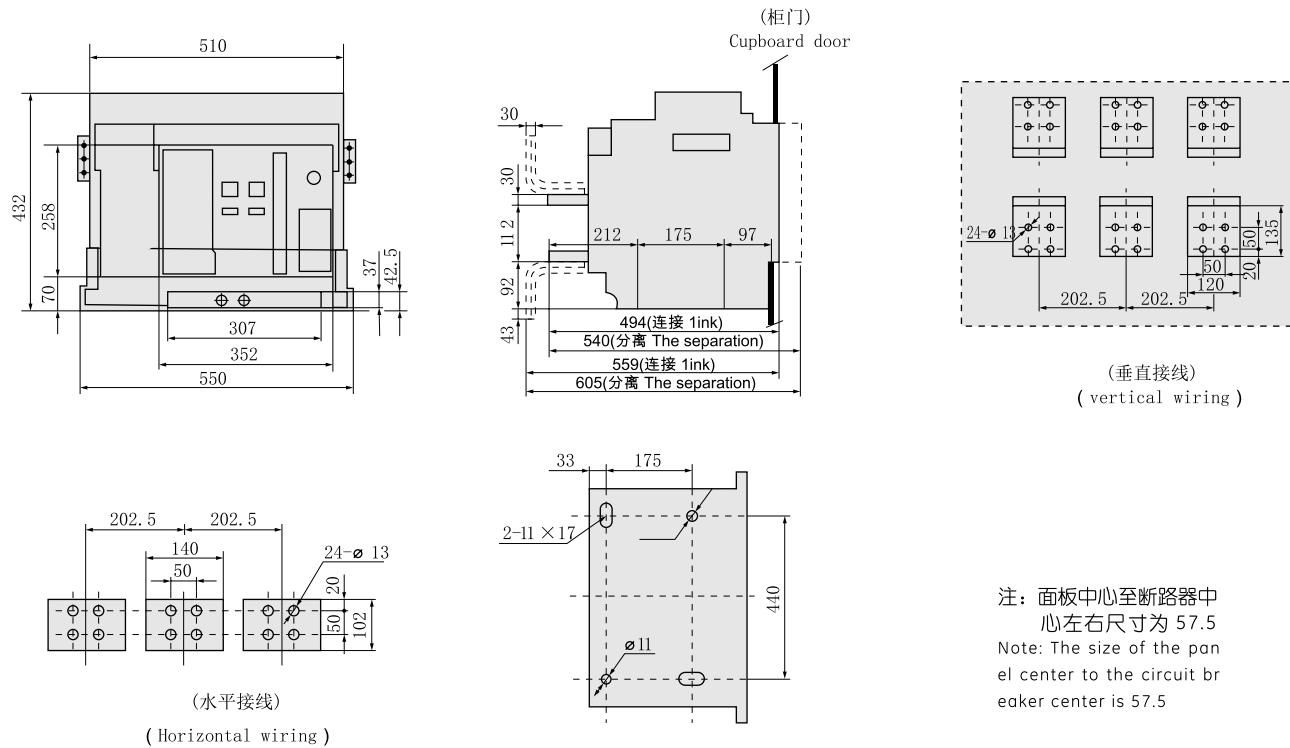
抽屉式断路器安装尺寸及外形尺寸 (STW6-4000)
